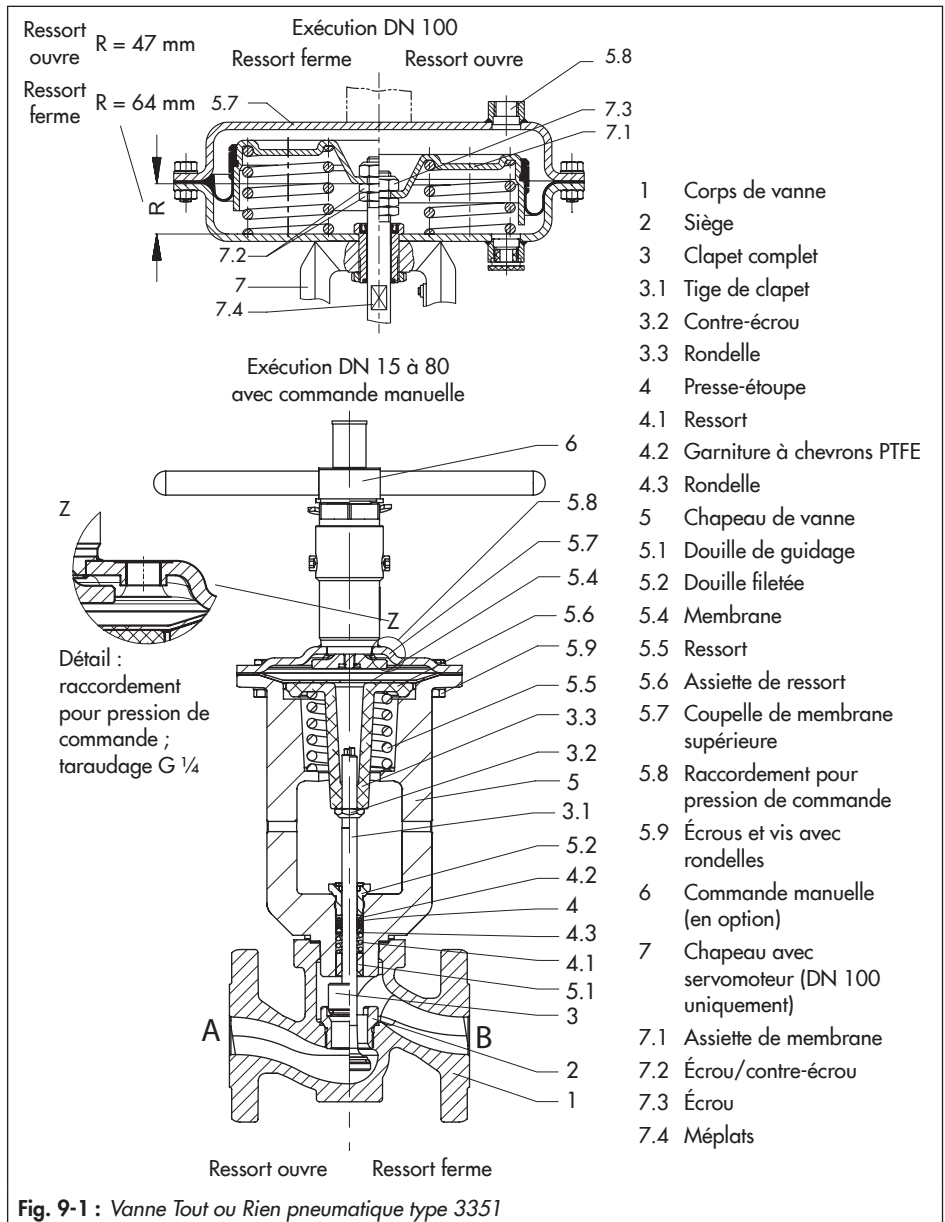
Vanne Tout ou Rien pneumatique type 3351
